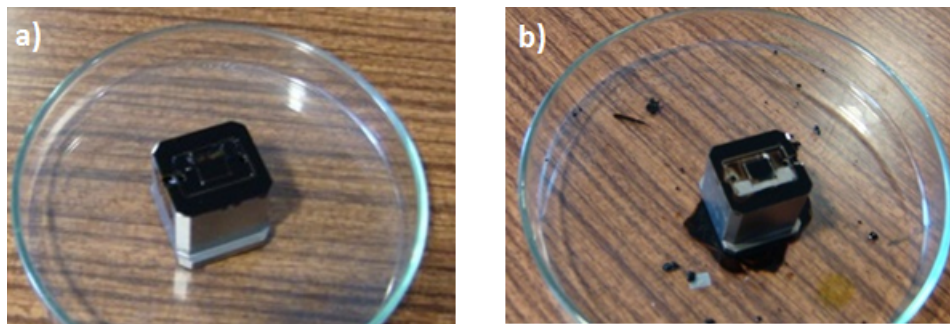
Representação prática da seguinte metodologia: a) Aplicação da cera preta sobre a superfície do bloco de moldação; b) Bloco de moldação com a primeira máscara removida, revelando a superfície a ser revestida.
